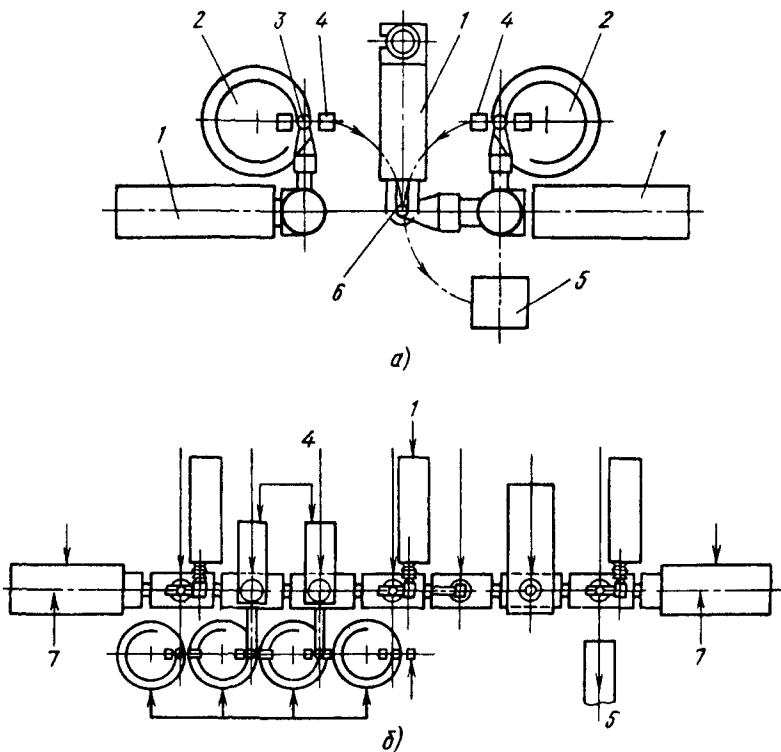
Компоновка сборочного автомата (а) и линии (б) из агрегатных модулей
